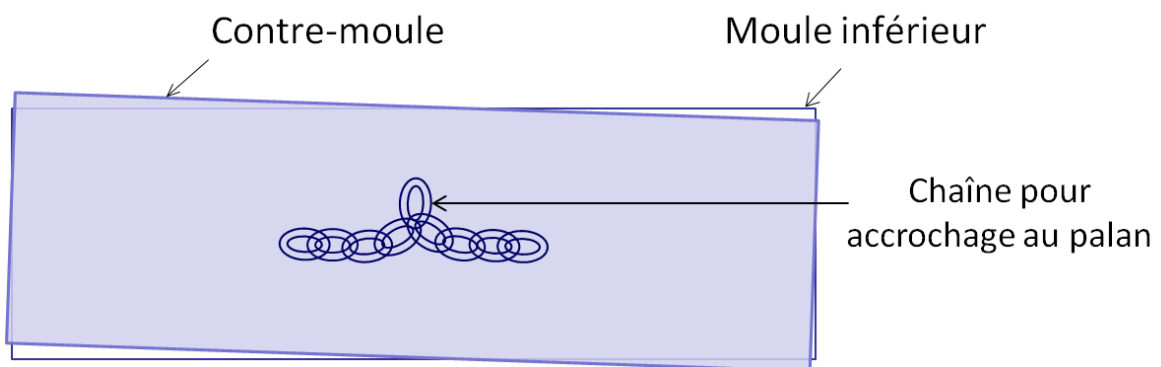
Illustration de mauvais positionnement du contre-moule sur le moule inférieur (vue du dessus).
